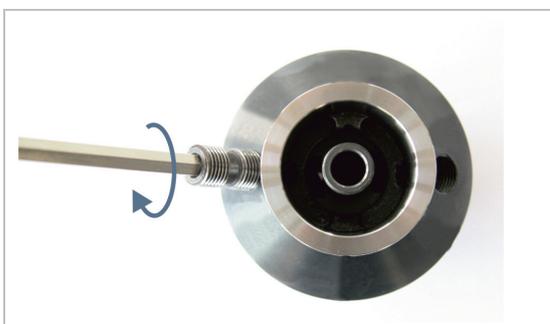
Einschrauben der Stützschraube in Anschlusskontur der Maschinenspindel
